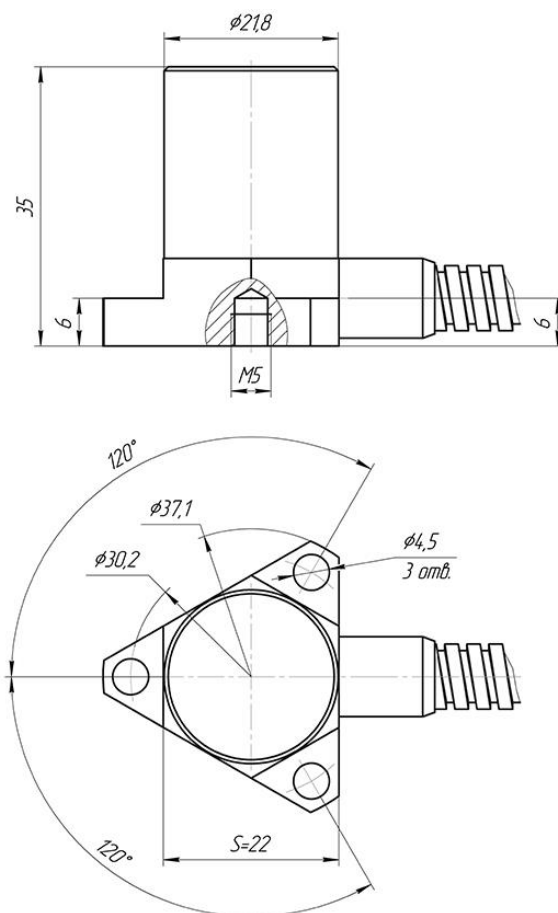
Габаритный чертеж велосиметра ZET 114
